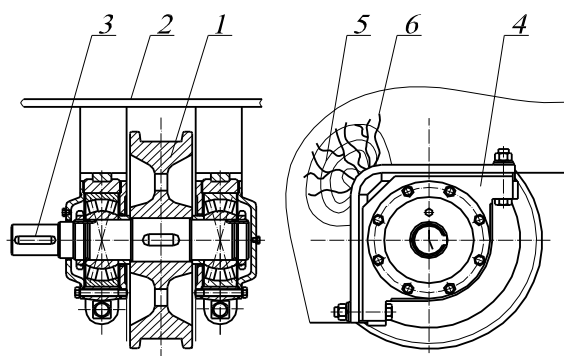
Конструкция ходовой части механизма передвижения крана: 1 – ходовое колесо; 2 – концевая балка; 3 – приводной вал; 4 – букса; 5 – платики; 6 – концентрация напряжений, трещины
